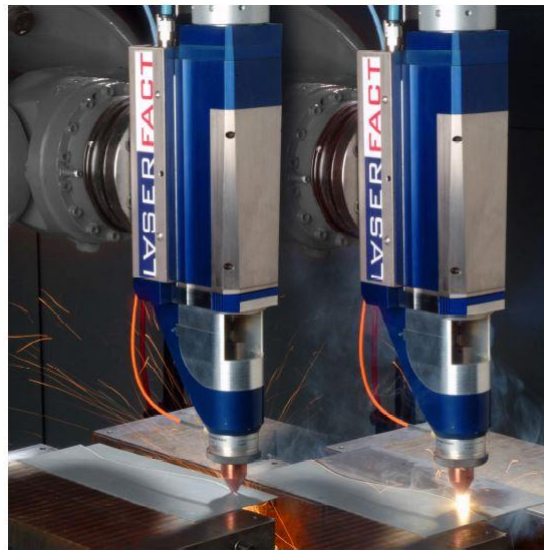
Cabeça de corte e soldadura Laserfact F2-Y; retirada de [8]
